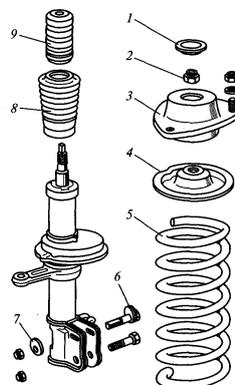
Элементы передней подвески: 1 — защитный колпак; 2 — гайка; 3 — верхняя опора стойки; 4 — верхняя чашка пружины; 5 — пружина передней подвески; 6 — регулировочный болт; 7 — эксцентриковая шайба; 8 — защитный кожух; 9 — буфер хода сжатия
